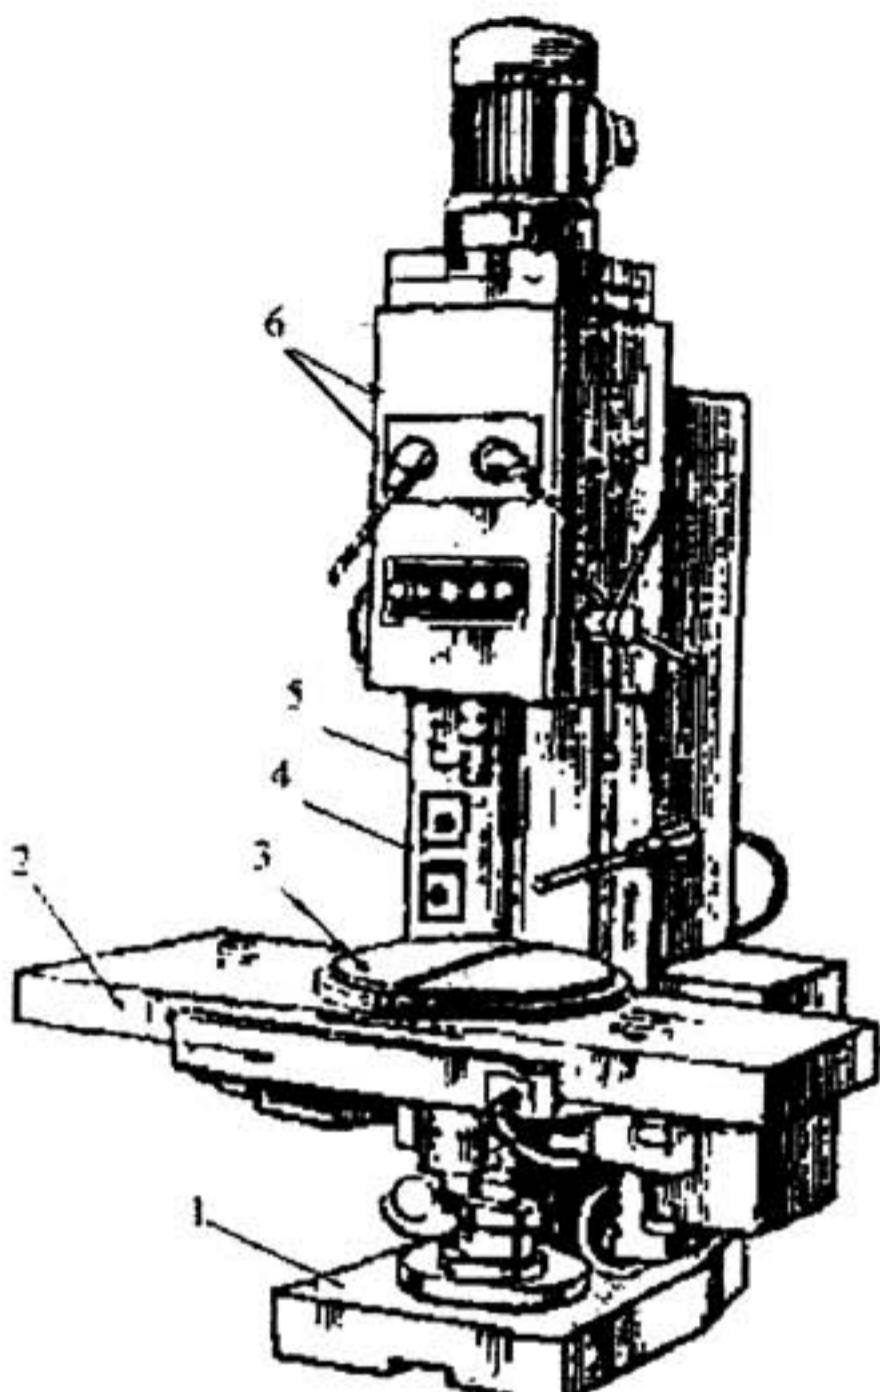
Внешний вид станка мод. 2Н135-1:
